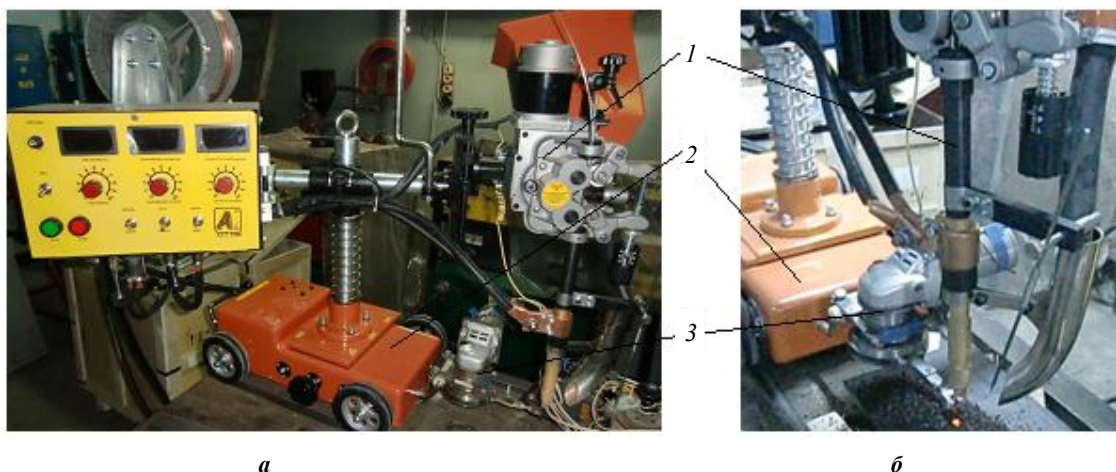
Варианты размещения на сварочном тракторе генератора импульсных перемещений электродной проволоки: *а* – поперек наплавляемого валика; *б* – вдоль валика; 1 – сварочная головка; 2 – каретка трактора; 3 – механический генератор
